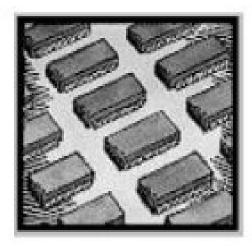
Montaje de los chips de memoria sobre la motherboard.
